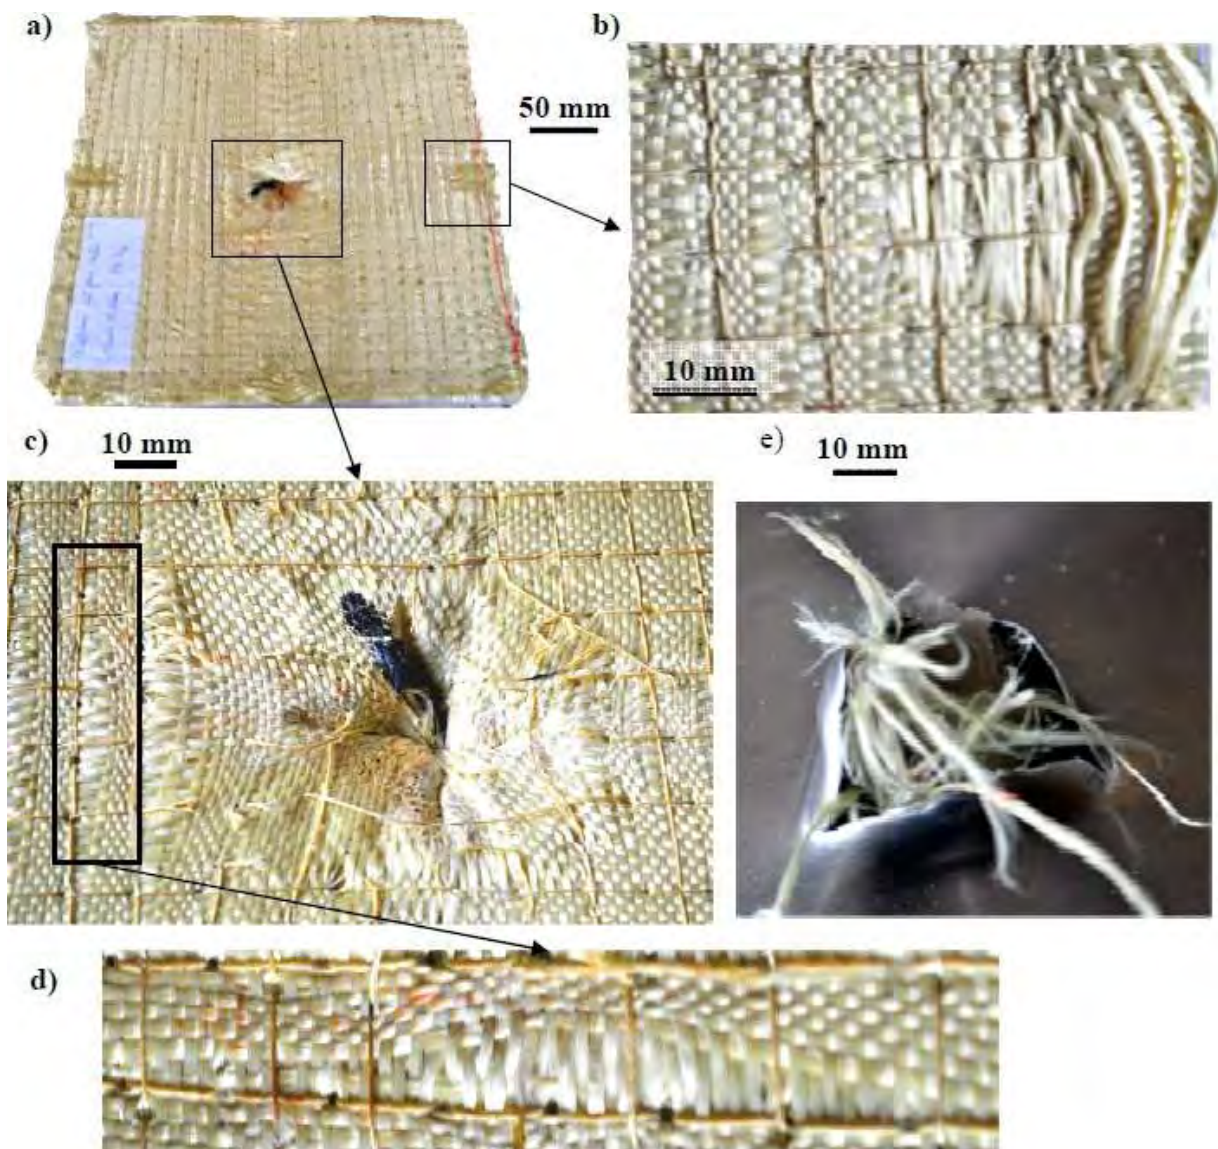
Echantillon $[P_{12}F_{30}A_1]_{300}$ après impact ; a) Vue de face ; b) Zoom sur les bords face avant ; c) Zoom sur le centre face avant ; d) Zoom sur le glissement des mèches ; e) Zoom face arrière
